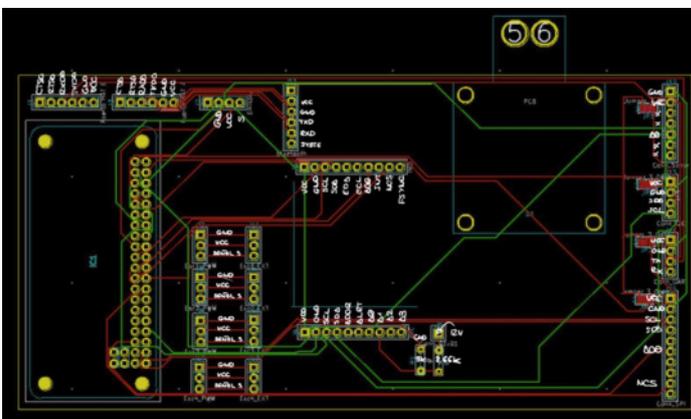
Diseño KiCAD de la tarjeta actualmente implementada en el dron
